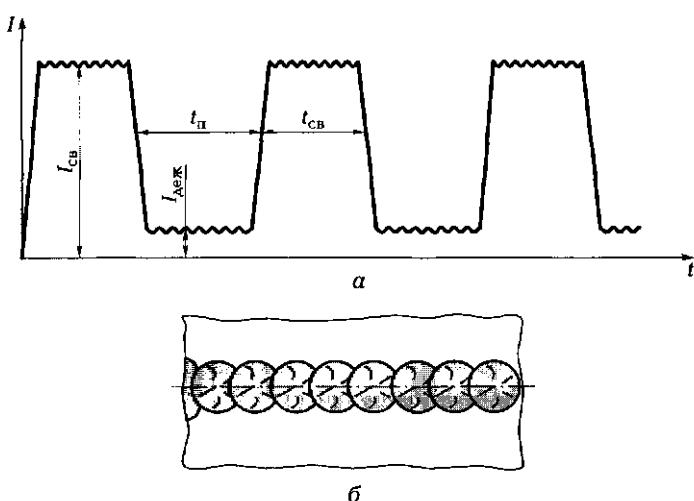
График импульсов сварочного тока (а) и форма сварного шва (б) (вид сверху):
